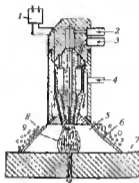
Схема подводной кислородной резки с воздушным пузырем: 1 — запальник; 2 — трубка для подачи режущего кислорода, 3 — трубка для подачи горючей смеси; 4 — трубка для подачи воздуха, 5 — воздушный пузырь; 6 — поток воздуха; 7 — разрезаемый металл, 8 — пламя, 9 — пузырьки воздуха
